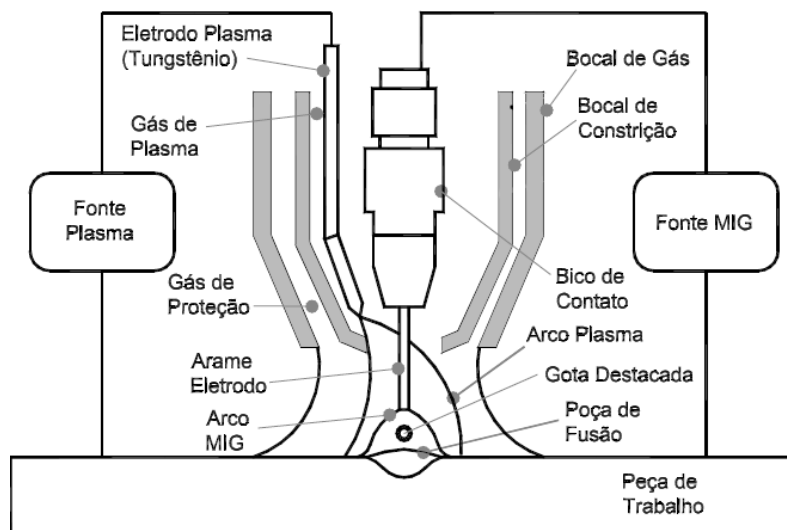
Desenho esquemático da pistola de soldagem Plasma-MIG com eletrodo de tungstênio (ESSERS, 1972, apud OLIVEIRA, 2006)
